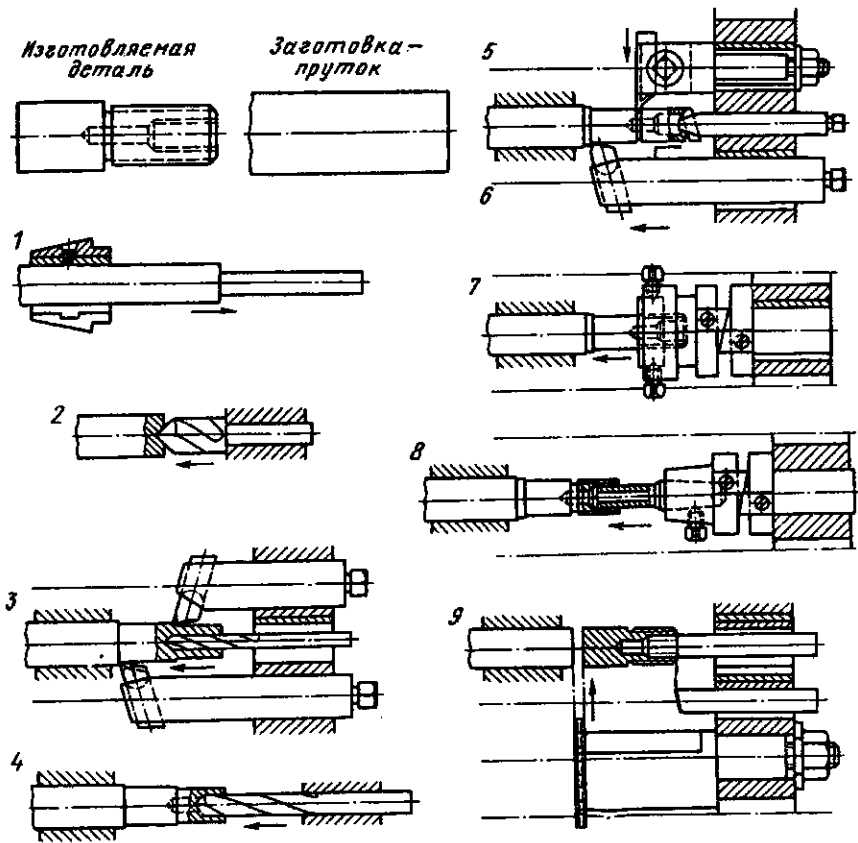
Схема обработки заготовки на токарно-револьверном станке с горизонтальной осью вращения револьверной головки:
